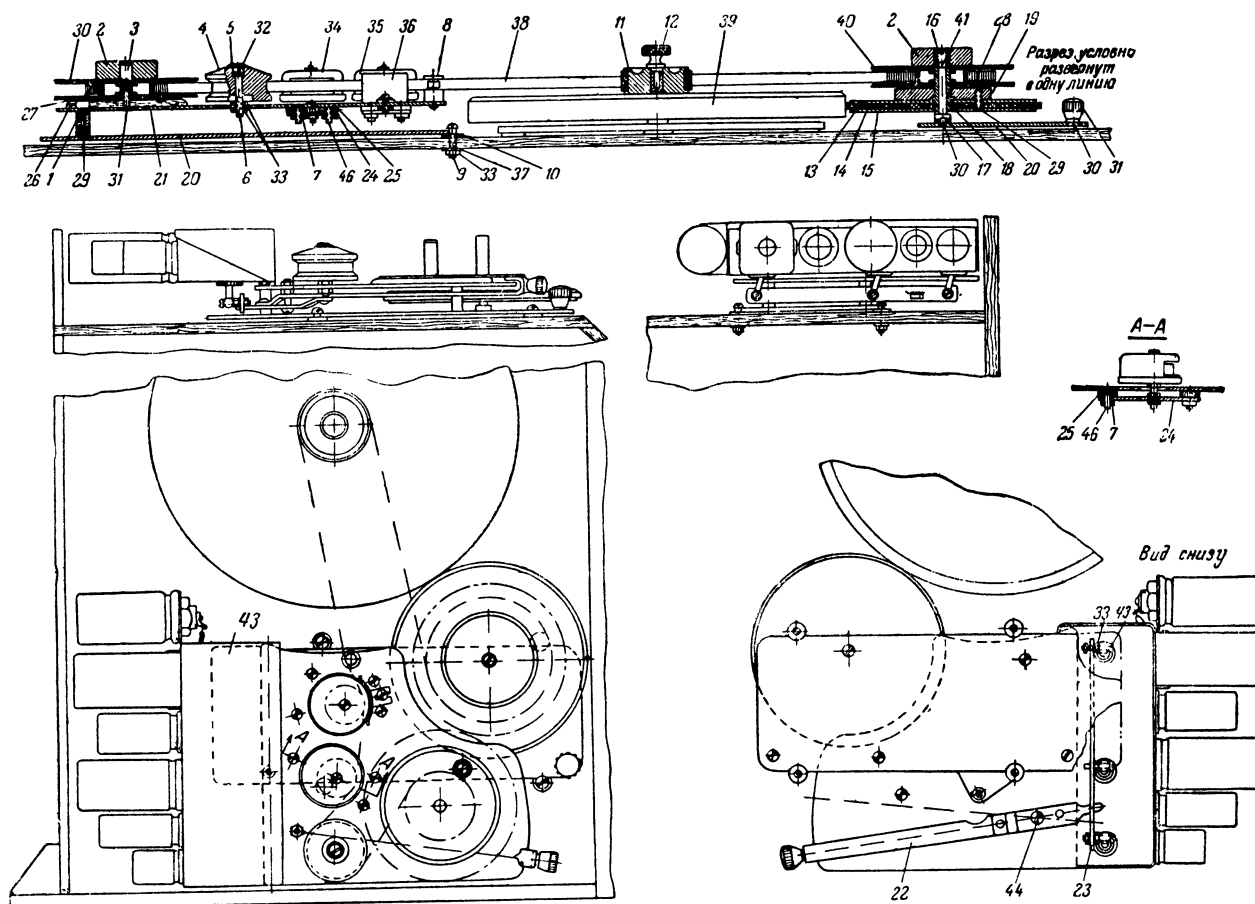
Чертеж лентопротяжного механизма магнитофона.
